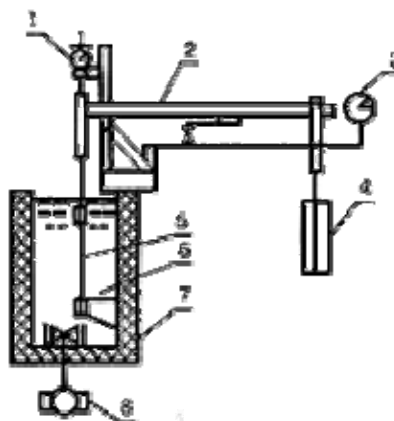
Схема испытания образцов сварных швов полиэтиленовых труб на длительное растяжение
